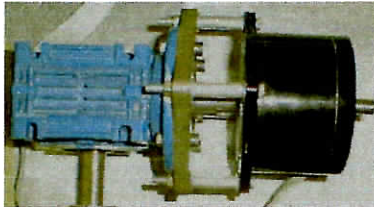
Acoplamento motor/redutor e suporte do motor
